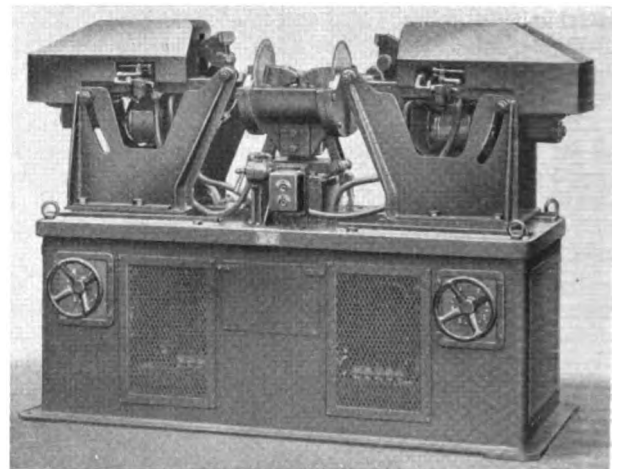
Selbsttätige Mehrfach-Stumpfschweißmaschine
